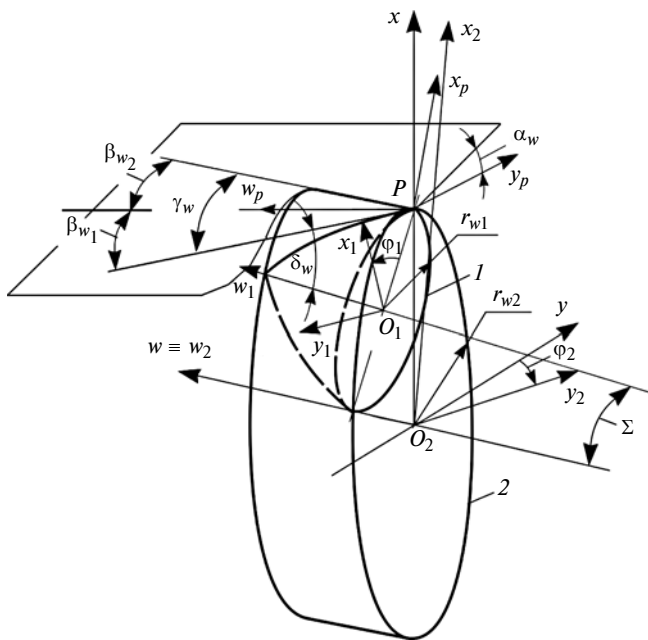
Схема цилиндро-конической зубчатой передачи внутреннего зацепления (исходная)
